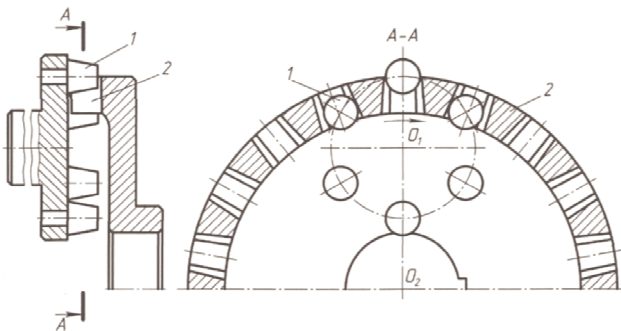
Конструктивная схема торцевой зубчатой передачи внутреннего зацепления.
